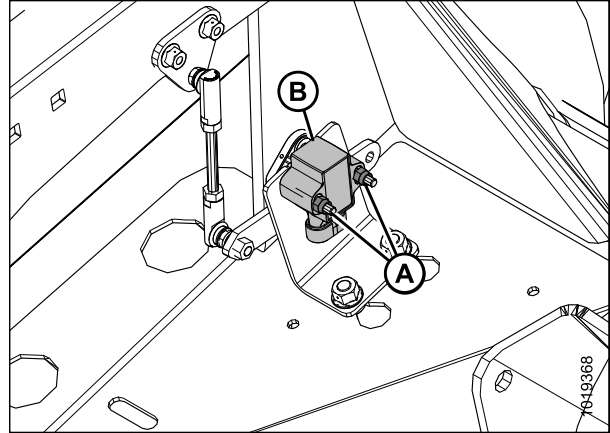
Sensor de altura del molinete - Molinete derecho Brazo
